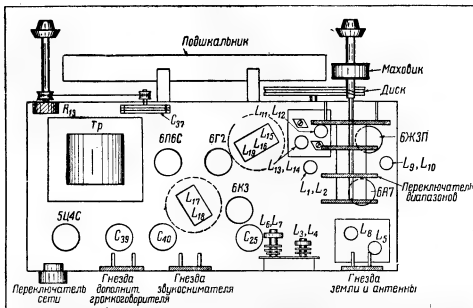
Схема расположения основных деталей на шасси приемника (вид снизу)
